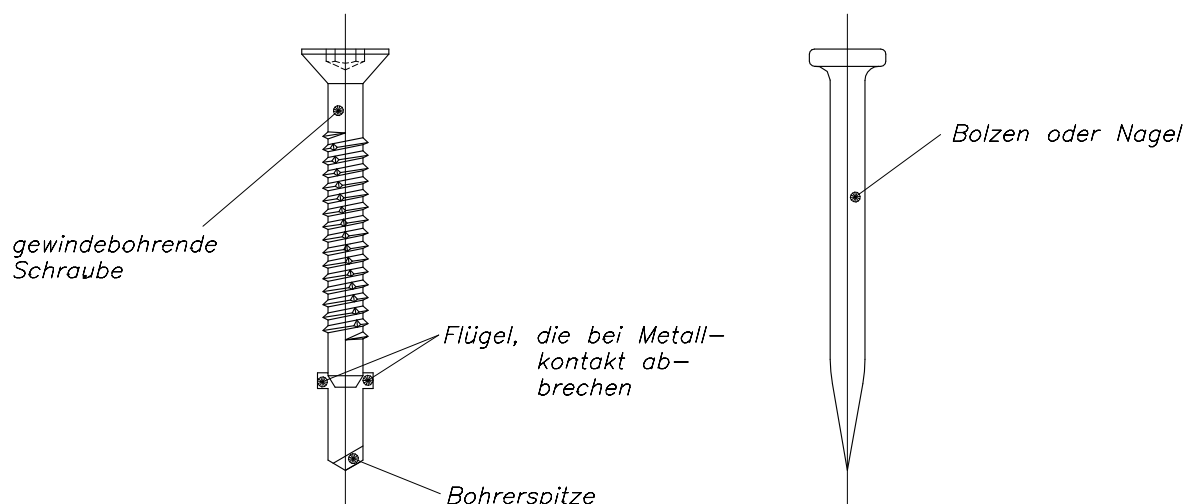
Gewindebohrende Schrauben, eingeschossene Bolzen oder Nägel
